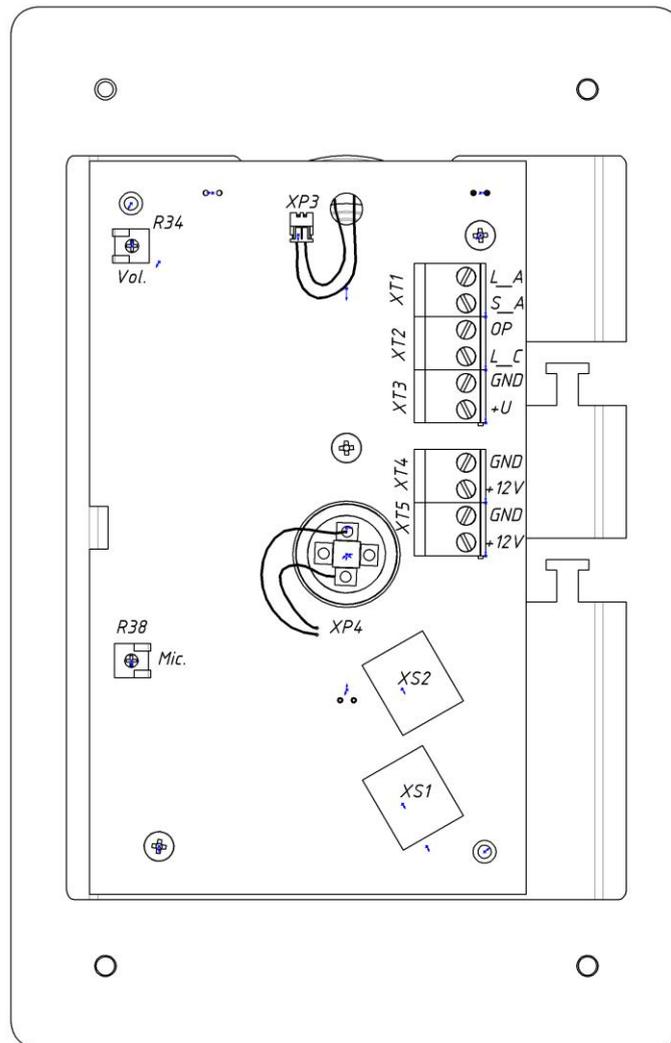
Внешний вид изделия DP1-UF8M-01 с задней стороны со снятой крышкой
